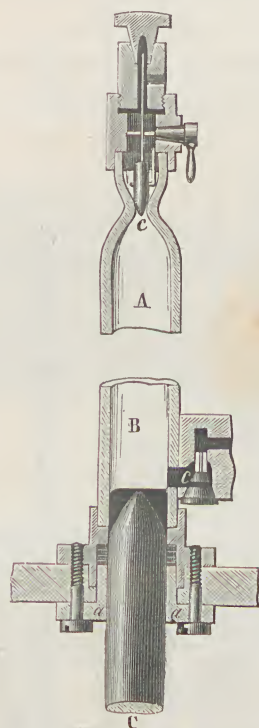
Detalles de un émbolo de la máquina de Kravogl
